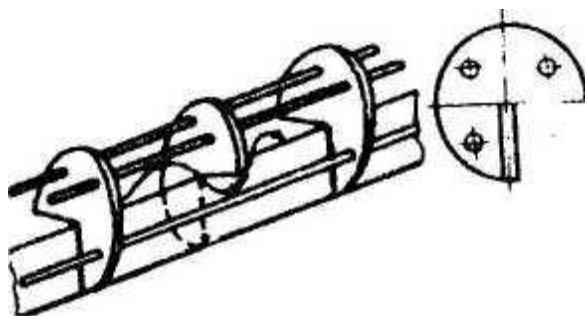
Конструктивная схема поперечных перегородок
